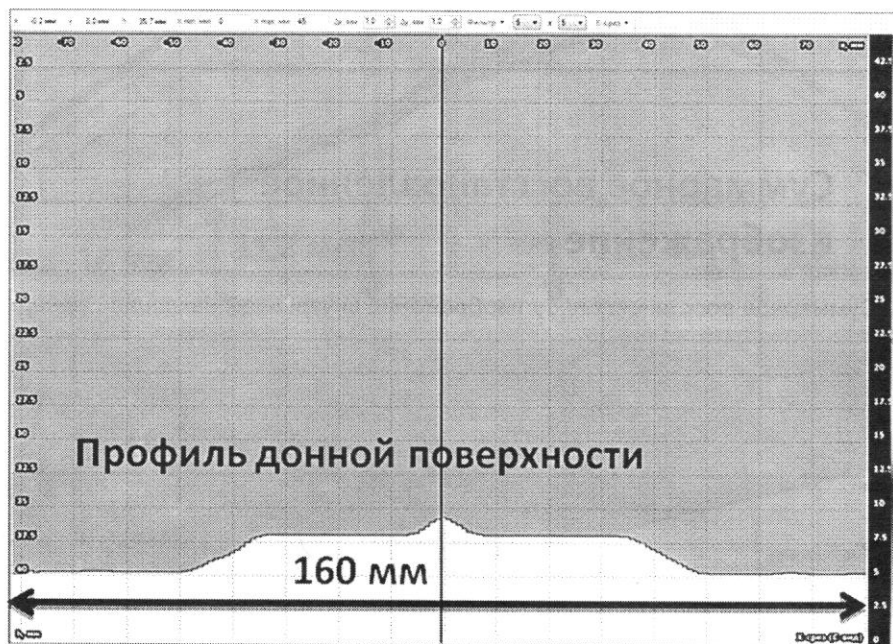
Профиль донной поверхности сварного соединения с вогнутым внутренним валиком
